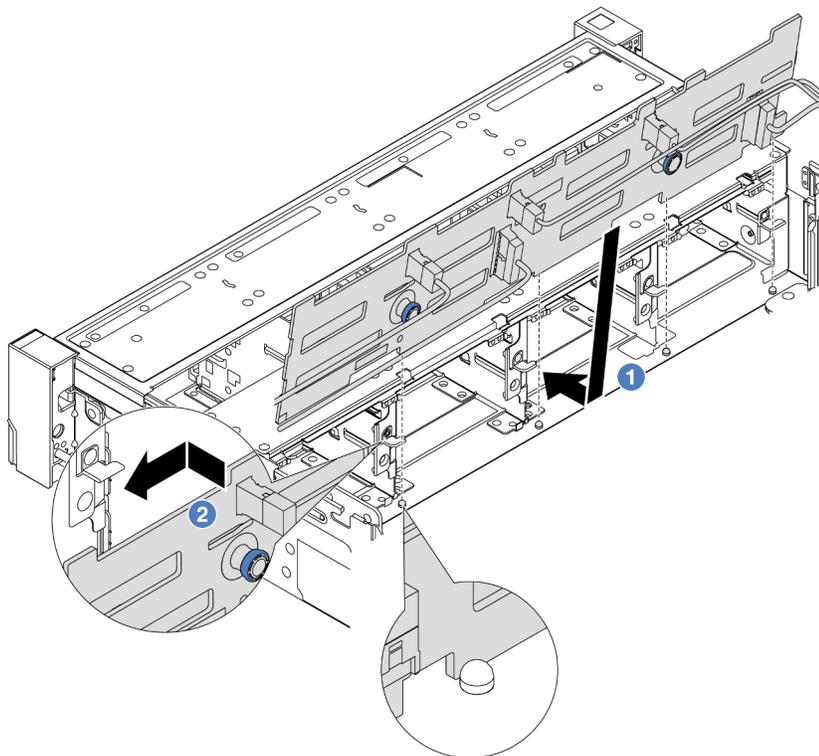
Installation d'un fond de panier d'unité 3,5 pouces
